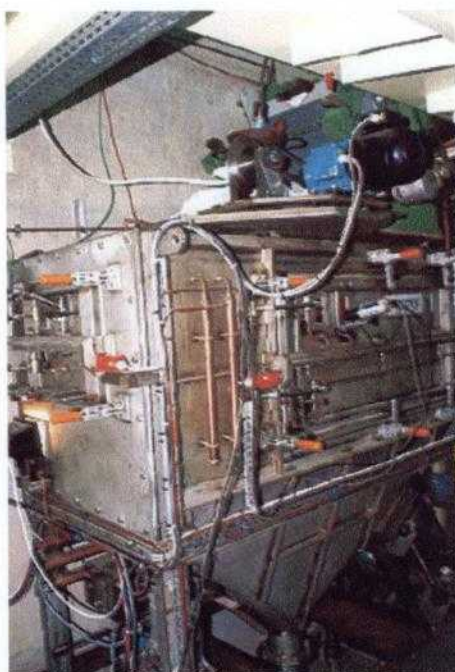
Fotografia da planta Osprey instalada no IPEN.
